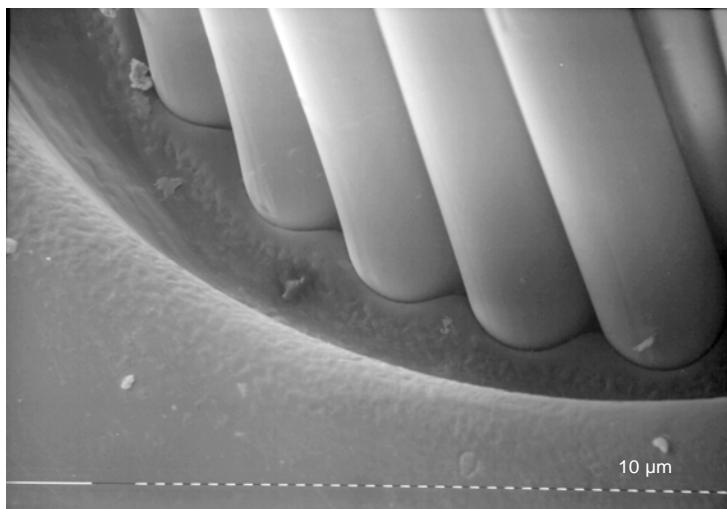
Prinzip 2 ( Produkt B): Teilansicht eines mit Kunststoff „eingeschweißten“ Borstenbündels
